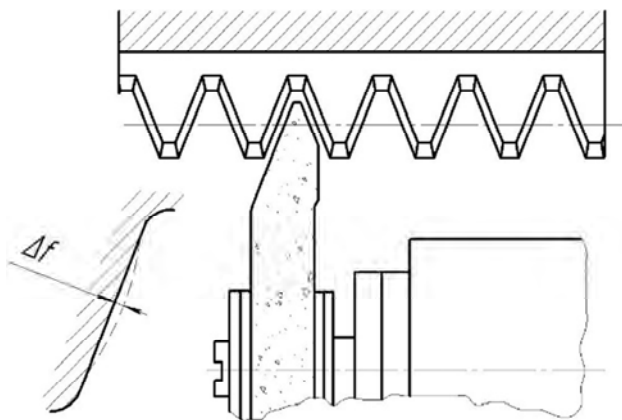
Искажение профиля зуба фрезы при затыловании дисковыми шлифовальными кругами
